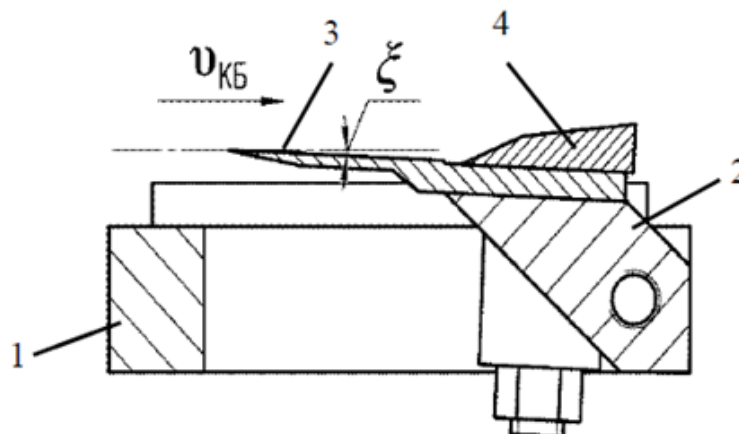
Ножова рама з плоским ножом: 1 – основа ножової рами; 2 – поворотна стійка; 3 – плоский ніж; 4 – притискна планка.
